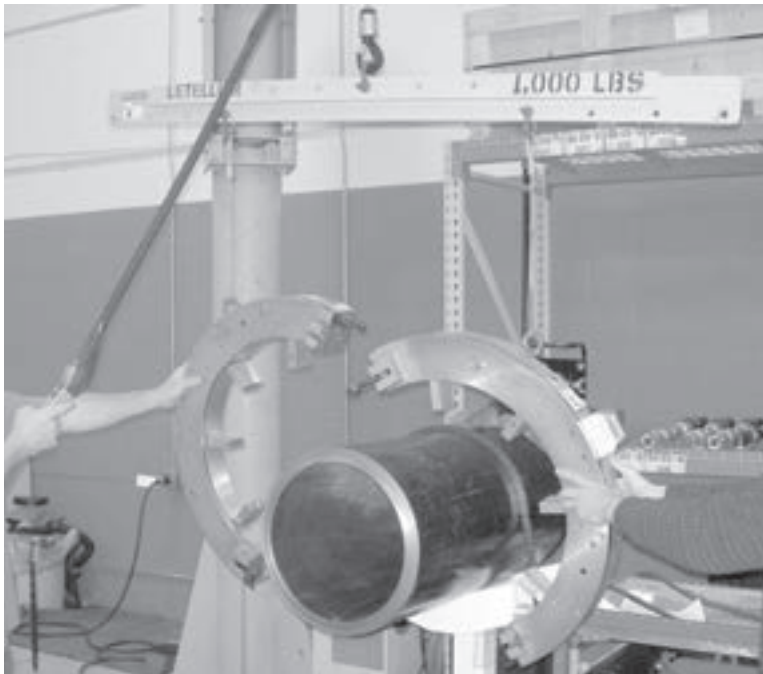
Ensamble las mitades del anillo alrededor del tubo como se muestra.
